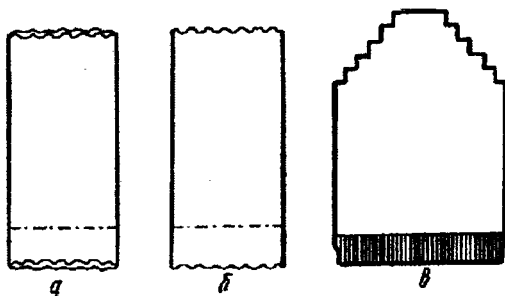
Формы купонов и деталей для изготовления полурегулярных
